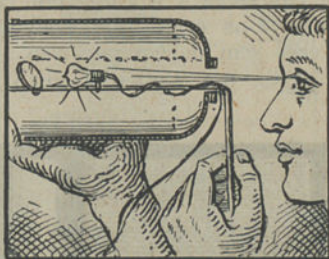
Exame da penetração da soldadura no interior dum recipiente.
